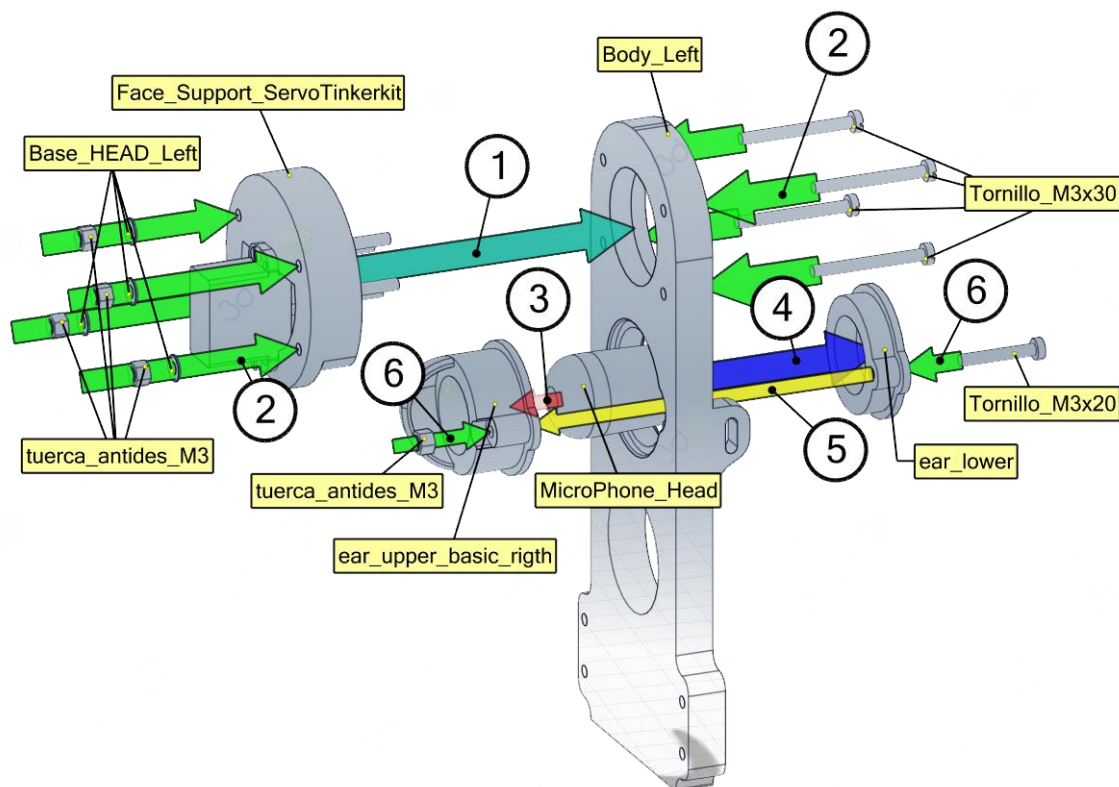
Paso 3: Montaje final Panel Lateral Izquierdo
